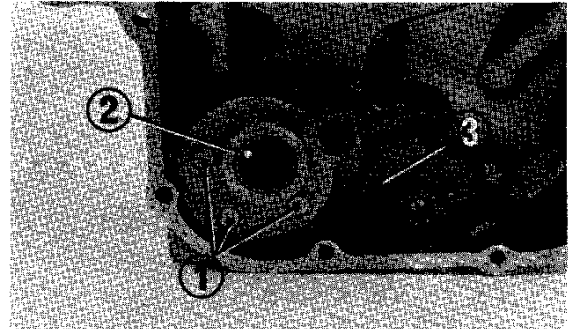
(1) Kühlwasserpumpe-Befestigungsschrauben
